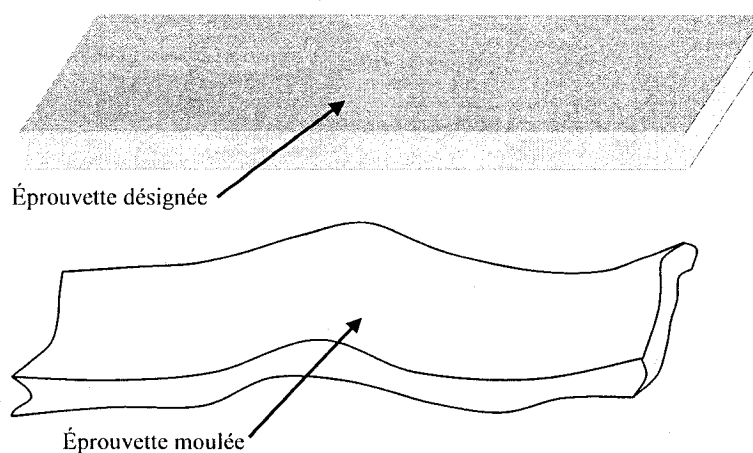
Vue générale de la déformation d'une éprouvette moulée.
